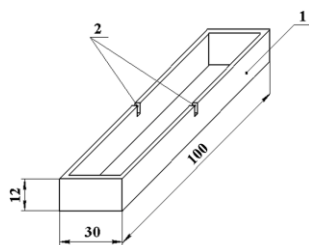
Прямоугольная форма для изготовления контрольного образца
